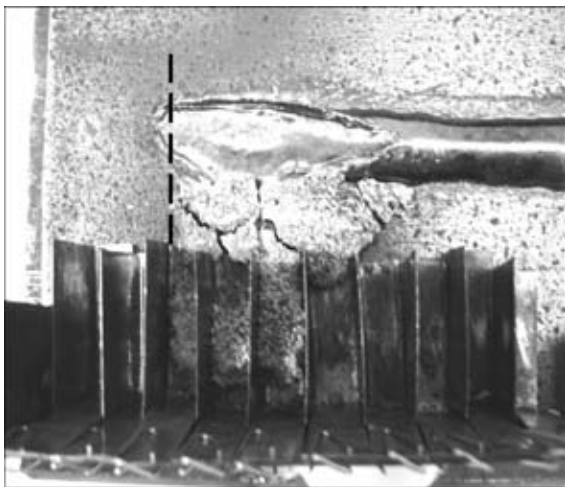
Распределение расплавленного шлака вдоль сварочной ванны при электродуговой сварке после удаления нерасплавившегося флюса и шлаковой корки (фаза эксперимента)
